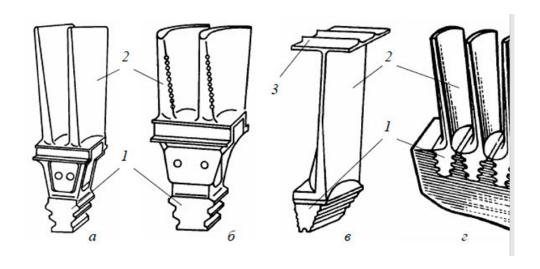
Рабочие лопатки газовых турбин: a, δ — газоохлаждаемые лопатки; ϵ — лопатки с бандажной полкой; ϵ — крепление рабочих лопаток в диске газовой турбины; ϵ — замок лопатки; ϵ — перо; ϵ — бандажная полка с уплотнительным гребнем
